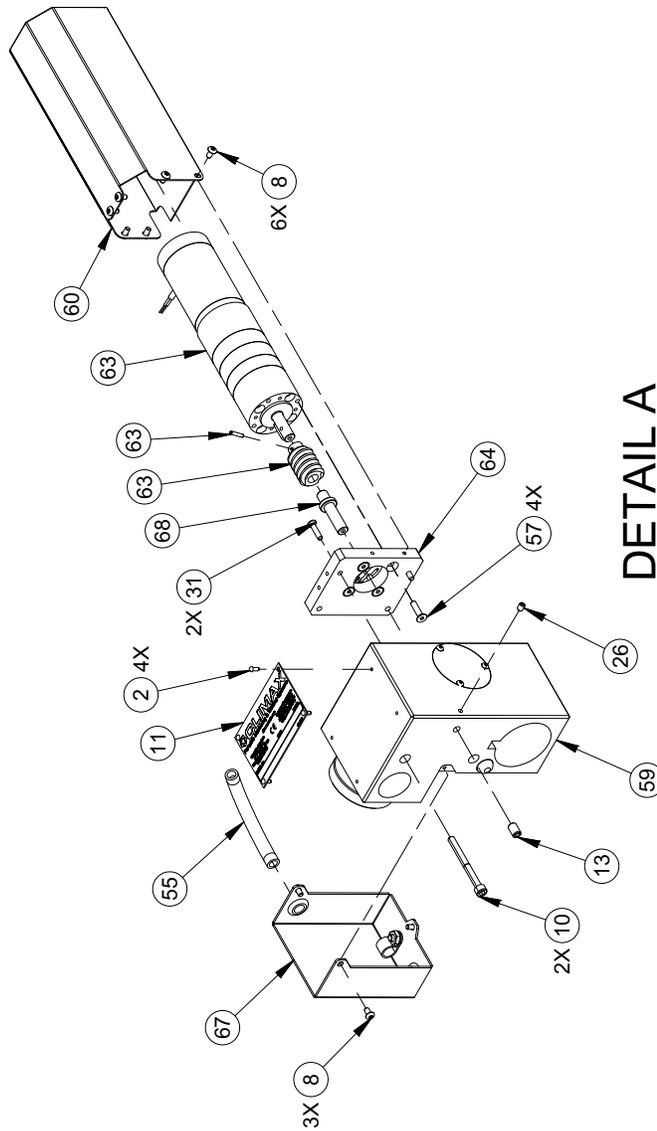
BW3000 ENSEMBLE (RÉF. 103159)
